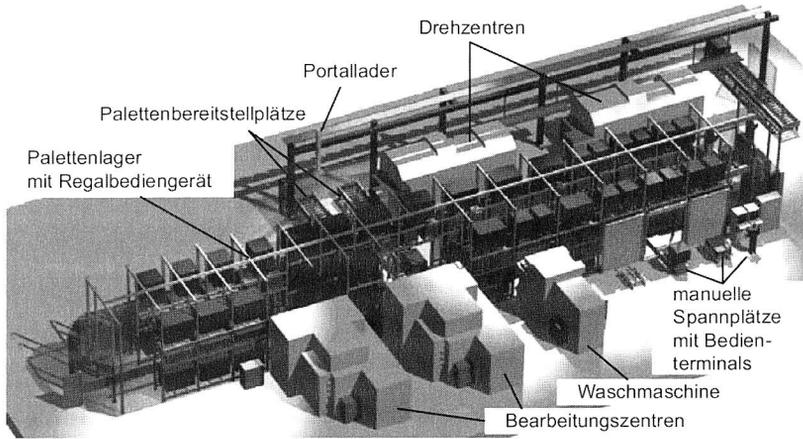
Flexibles Fertigungssystem für die Zerspantung, bestehend aus voll- oder teilautomatisierten Bearbeitungssystemen, die sich wiederum aus einer oder mehreren Bearbeitungsmaschinen, einem automatisierten Material- bzw. Teilelager und einer oder mehreren Be- und Entladestationen zusammensetzen. [17]
